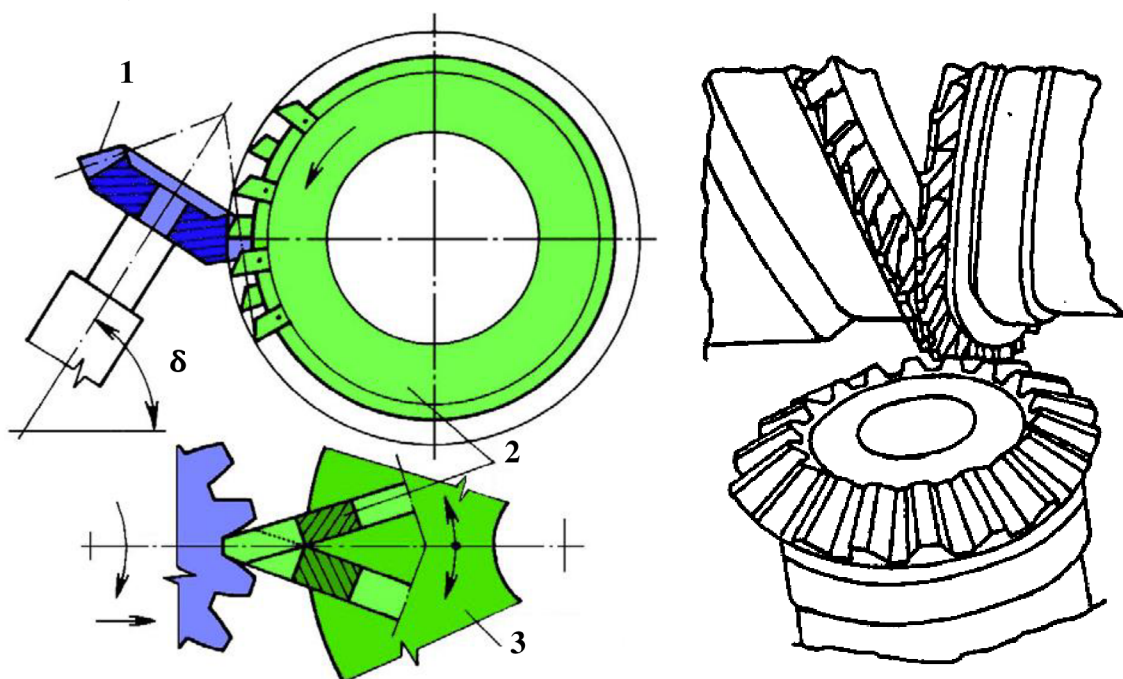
Frézování kuželových kol s přímým ozubením tvarovou kotoučovou frézou [18].
